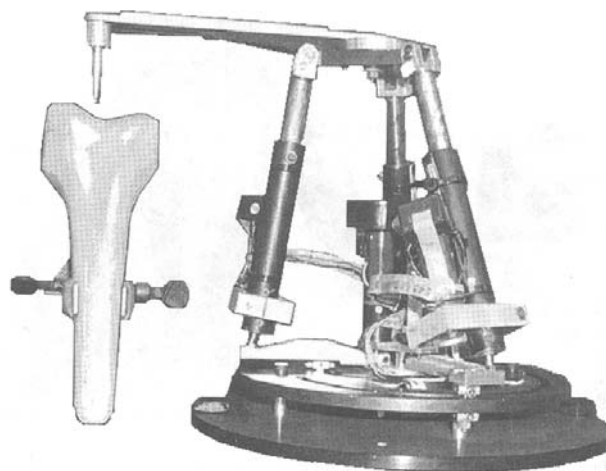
Загальний вигляд ВПК типу «трипод», який сканує поверхню складної форми
